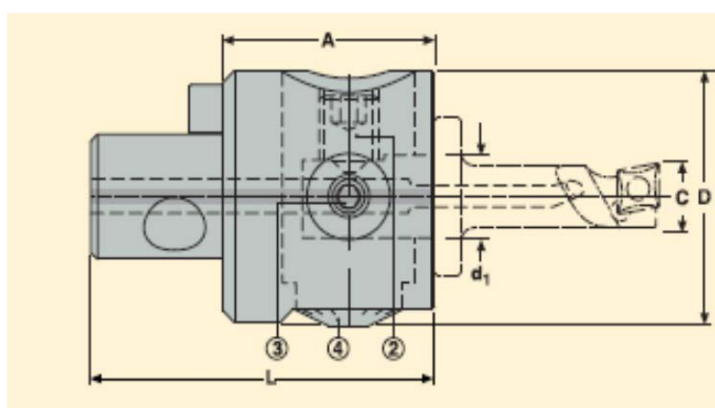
Головка для чистовой расточки ЕРВ 750
